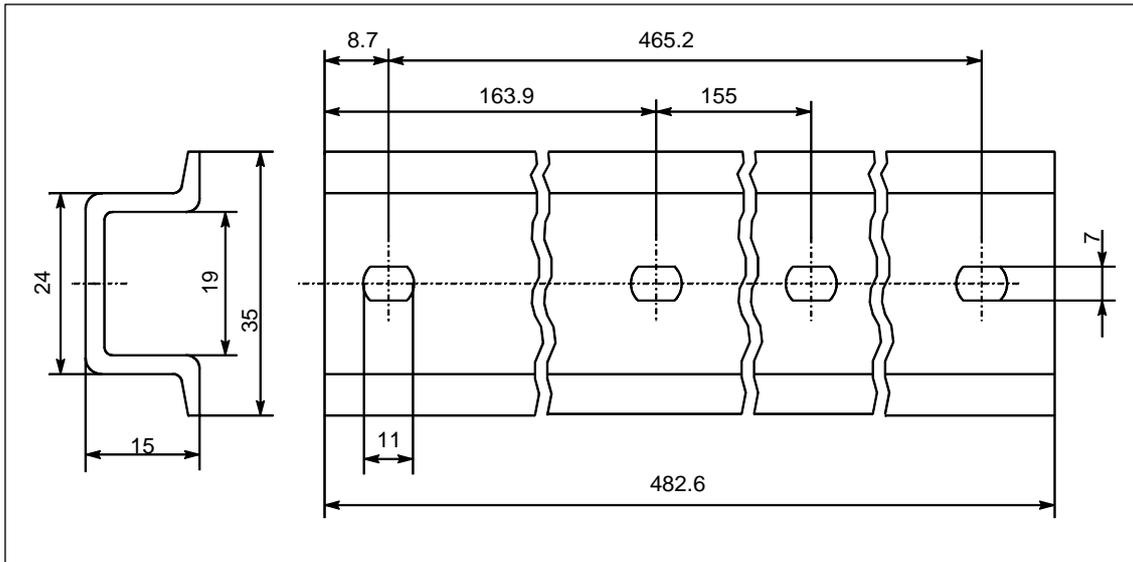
Чертеж с размерами 483-миллиметровой стандартной профильной шины
